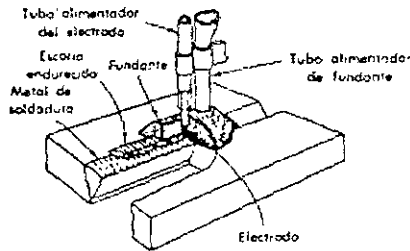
Vista de corte seccional de una soldadura con arco sumergido.
